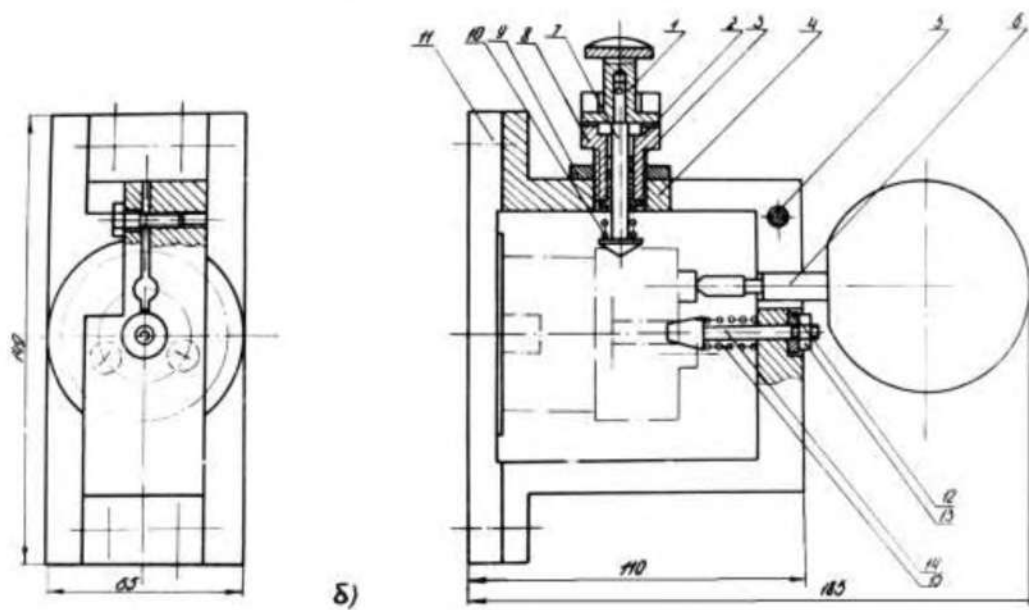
Загальний вид і конструкція пристрою для вимірювання зносу:
